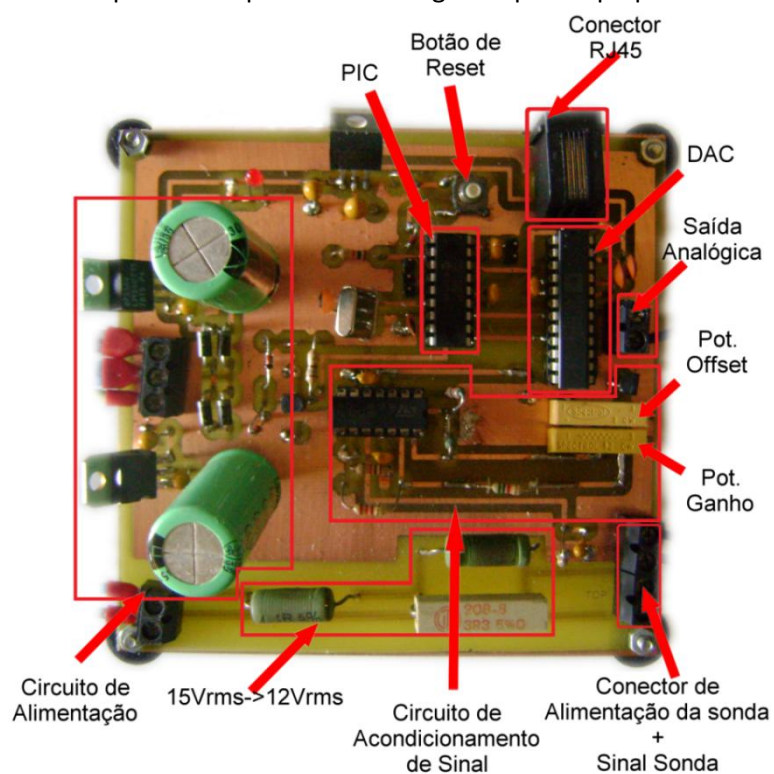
PLACA PCB DO MEDIDOR
